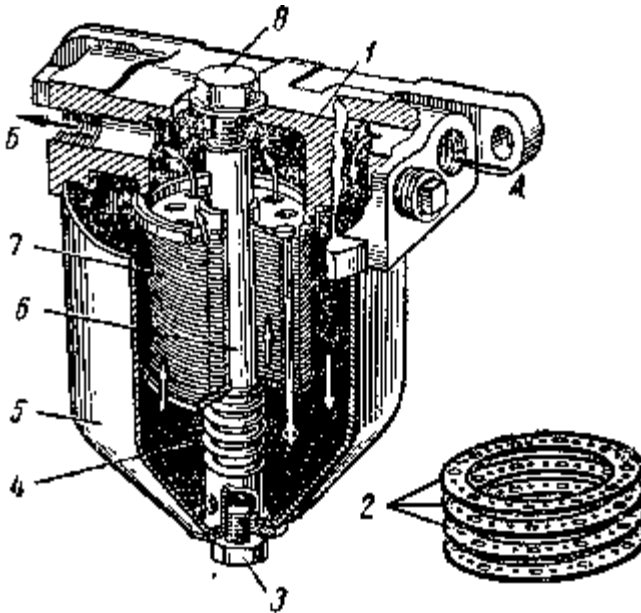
Фильтр-отстойник: 1 – корпус; 2 – латунные пластины; 3 – сливная пробка; 4 – пружина; 5 – отстойник; 6 – стержень; 7 – фильтрующий элемент; 8 – болт.
